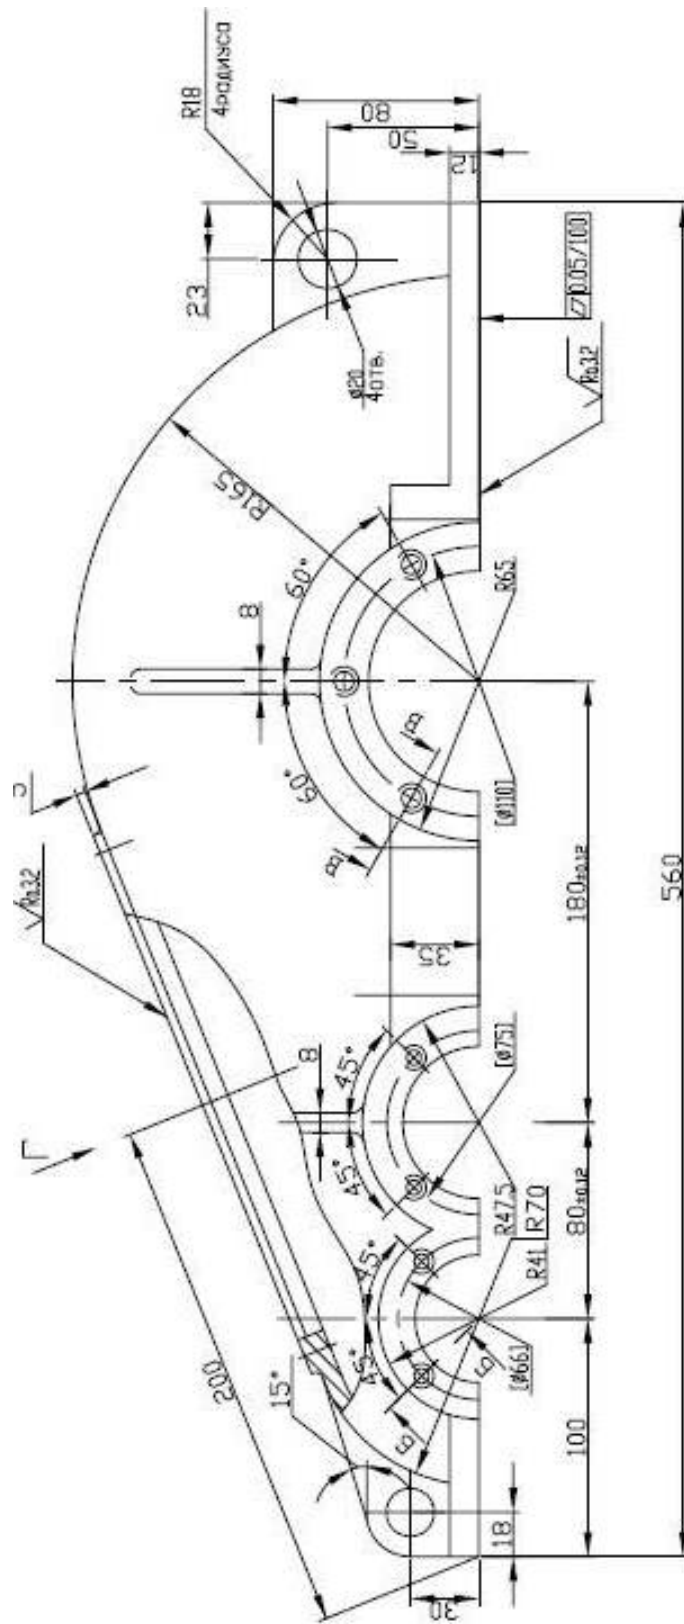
Укрупненный вид спереди на крышку редуктора на рисунке К.6
